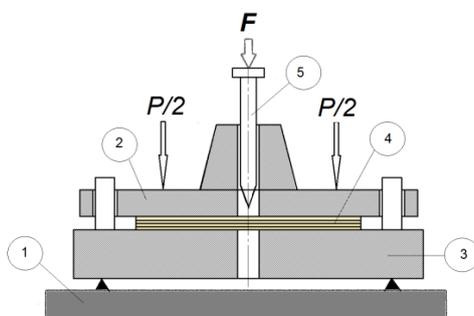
Схема устройства для прокола препрега (устройство для прогрева препрега не показано)
